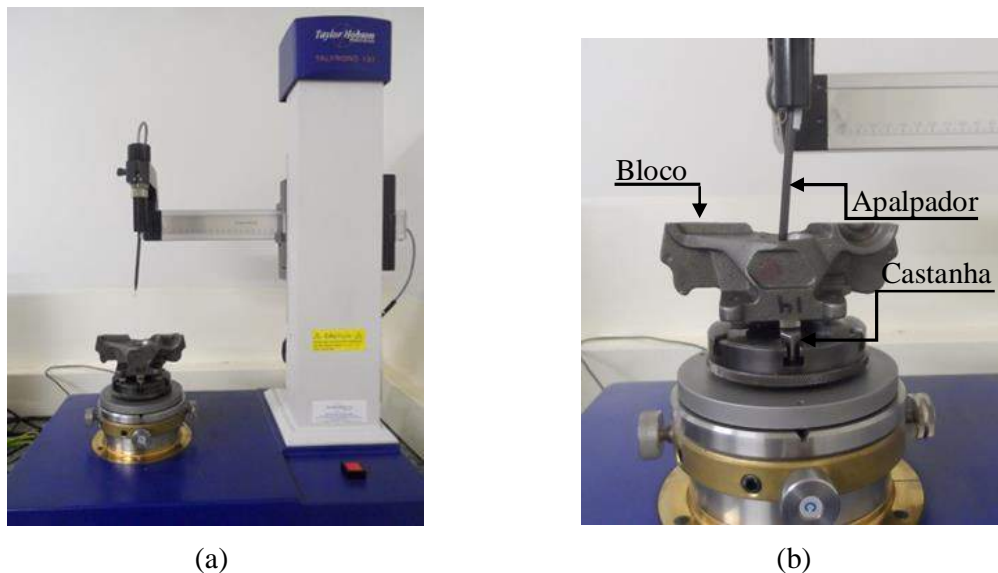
(a) Máquina de medir desvios de forma e (b) fixação do bloco após cortado.
